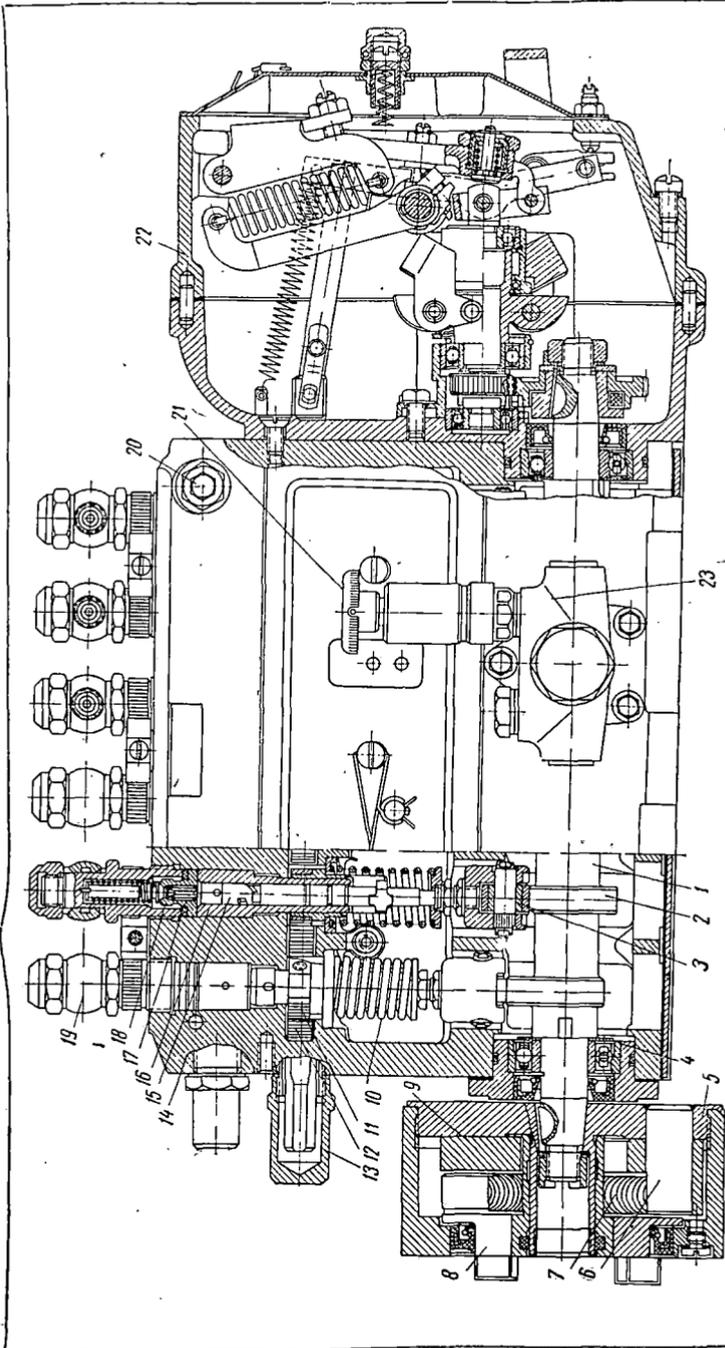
Топливный насос высокого давления: 5 — ведомый фланец автоматической муфты опережения впрыска топлива; 6 — шариковый толкатель; 4 — шариковый подшипник; 3 — кулачок; 2 — кулачок; 1 — кулачковый вал; 22 — гильза плунжера; 11 — зубчатый сектор; 12 — зубчатая рейка; 13 — ограничитель хода рейки; 14 — корпус насоса; 15 — плунжер; 16 — пружина плунжера; 17 — нагнетательный клапан; 18 — корпус клапана; 19 — штуцер; 20 — пробка для выпуска воздуха; 21 — ручной насос; 23 — регулятор числа оборотов коленчатого вала двигателя; 23 — топливopодкачивающий насос
